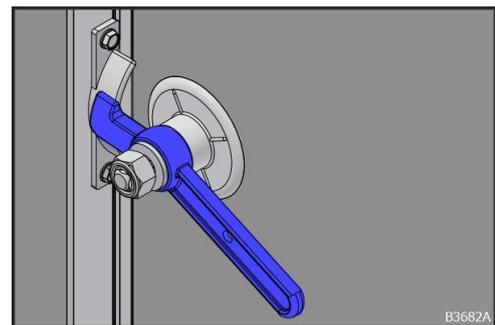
Nockenzunge mit Innenhebel (saugseitig)
